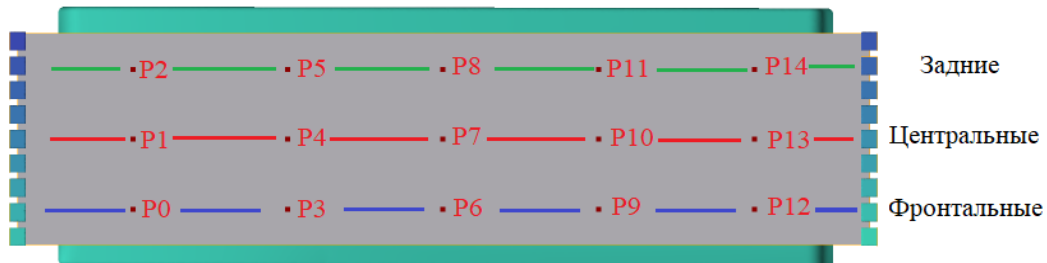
Условно выбранные точки на поверхности листовой заготовки для идентификации значений толщины оболочковой детали в системе QForm
